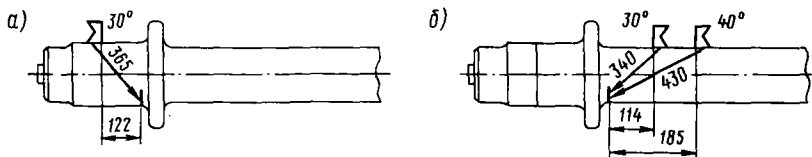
Схемы и зоны контроля наклонными искателями главного приводного вала эскалатора ЭТ-5 при различном расположении искателей (а, б) с левого торца вала
